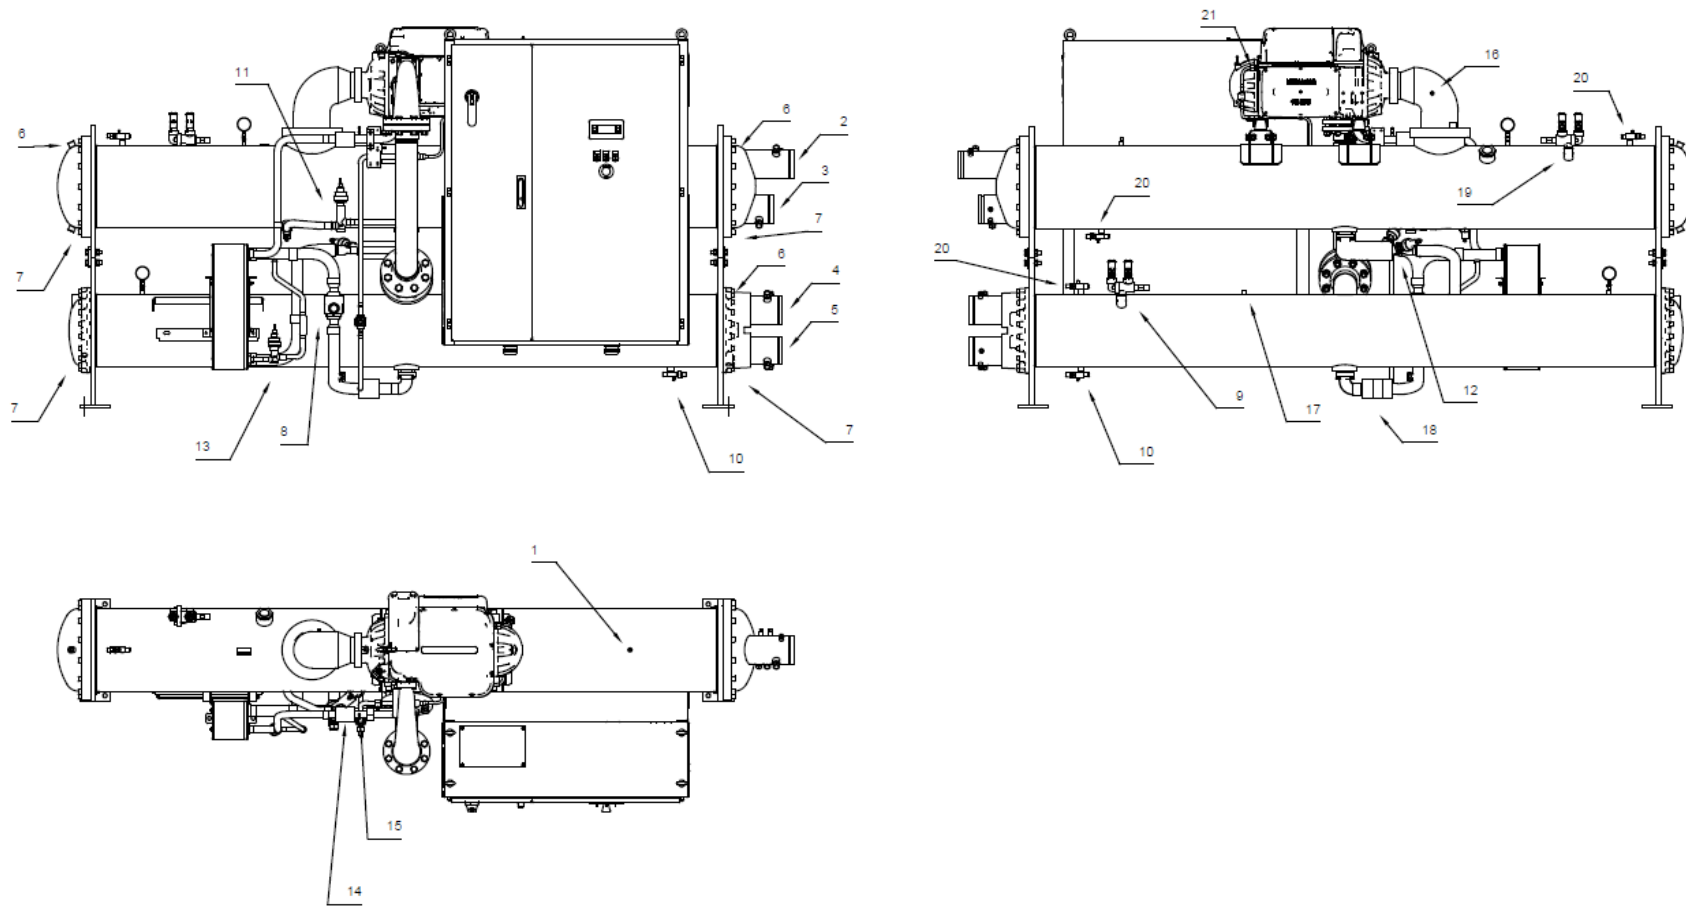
Beskrivningar av komponenter för enskild kompressorenhet
